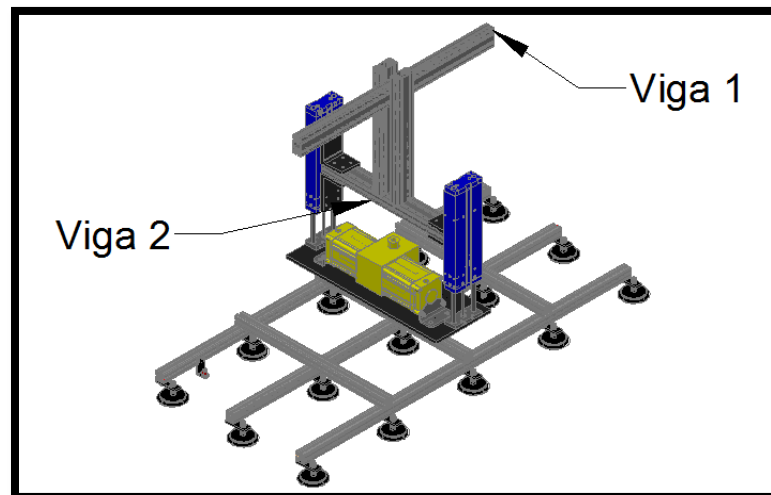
Viga 1 y viga 2 a diseñar.
